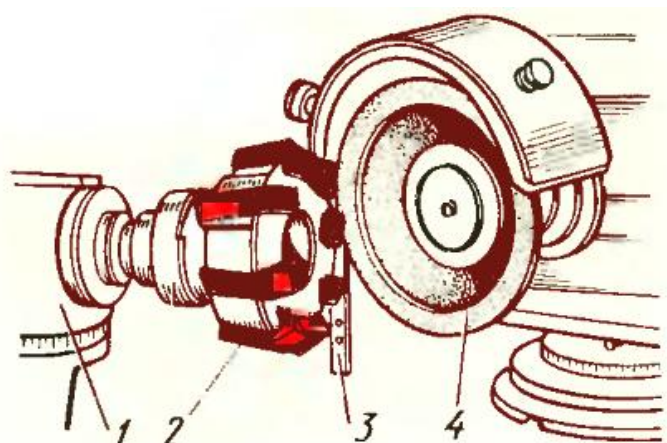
Заточка торцевой фрезы алмазным кругом: 1 — головка ваточного станка, 2 - торцевая фреза, 3 — упор, 4 — алмазный круг
